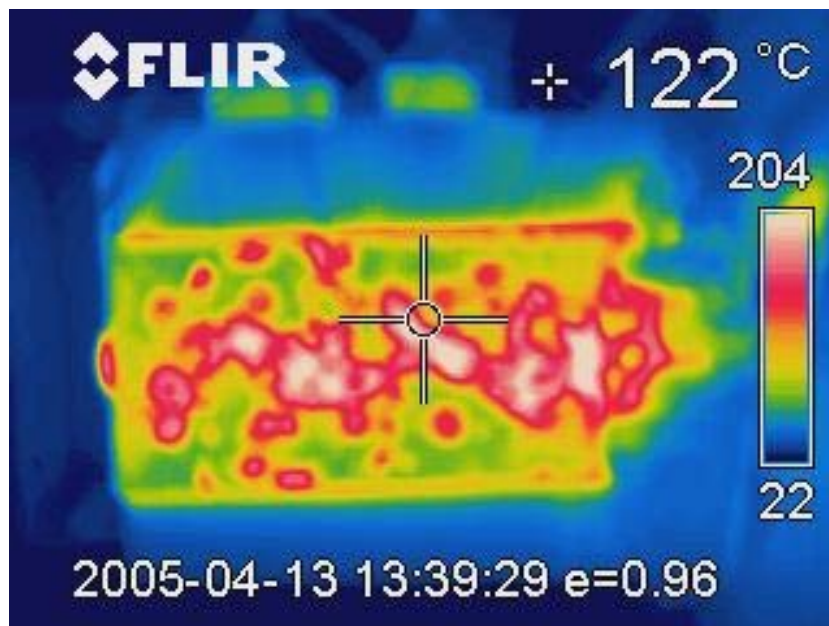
Photo IR de la filière vue de haut. En haut de la photo, on aperçoit les connecteurs.
